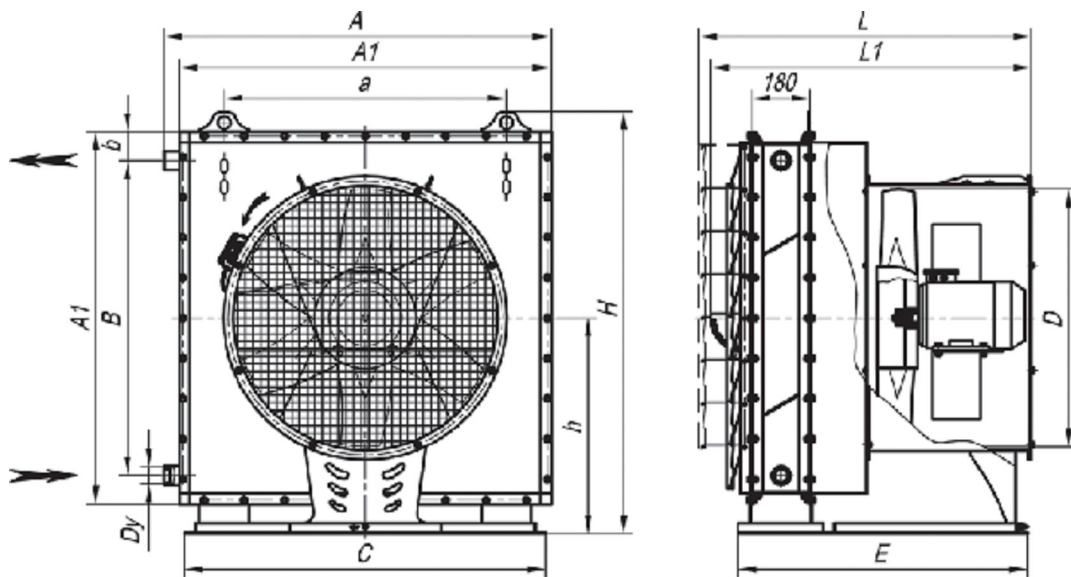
Габаритные и присоединительные размеры агрегатов воздушно-отопительных АО2 на базе калориферов типа КСк.
